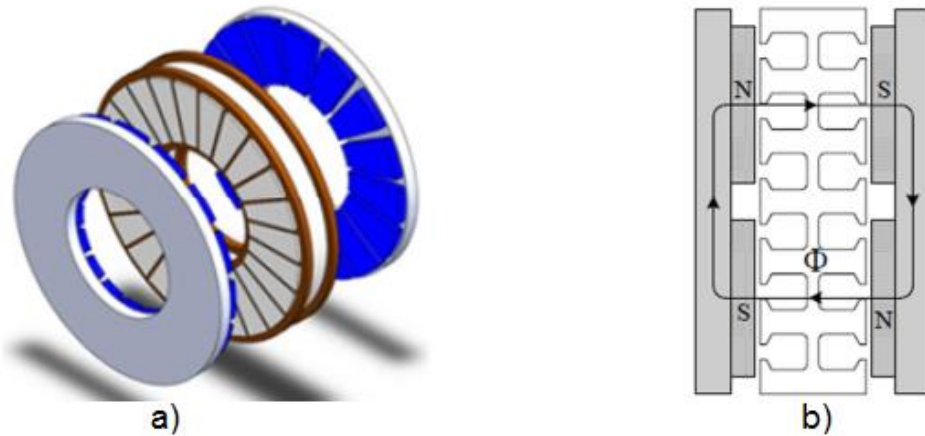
machine à flux axial stator double rotor a) avec stator encoché et bobinage réparti b) de type NS [23][22].
